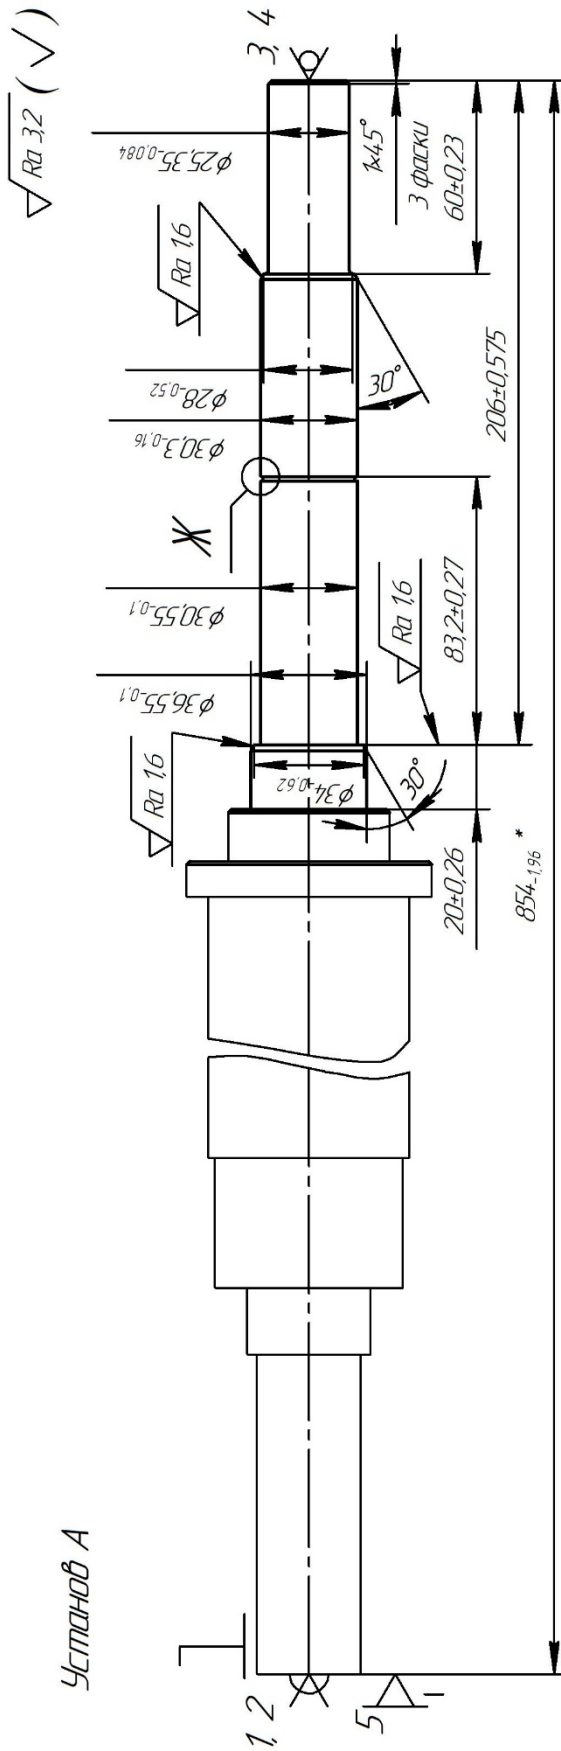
Схема базування заготовки на операції токарній з ЧПК 025, установ А
